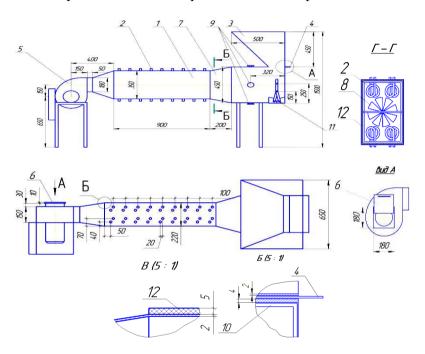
Чертеж устройства для тепловой обработки зерна:
